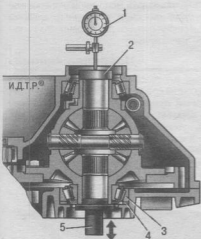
Схема подбора толщины регулировочного кольца подшипников дифференциала: 1 - индикатор; 2 - опорная пластина; 3 - подшипник дифференциала; 4 - установочное кольцо; 5 - оправка
